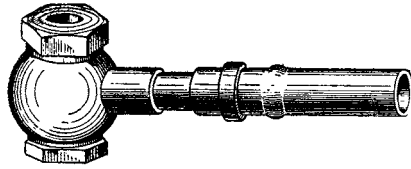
Приспособление КВ-сб. 85-98 для слива горячего из баков
